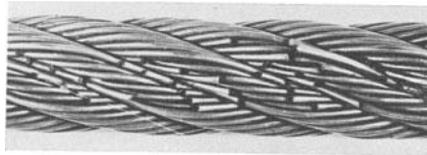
Dauerbiegeprobe mit Drahtbrüchen an einer Mantellinie.
